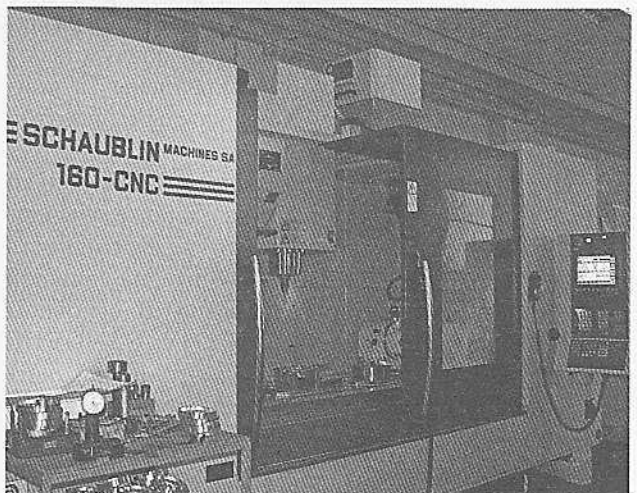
Вертикально-фрезерный станок Schaublin 160-CNC
